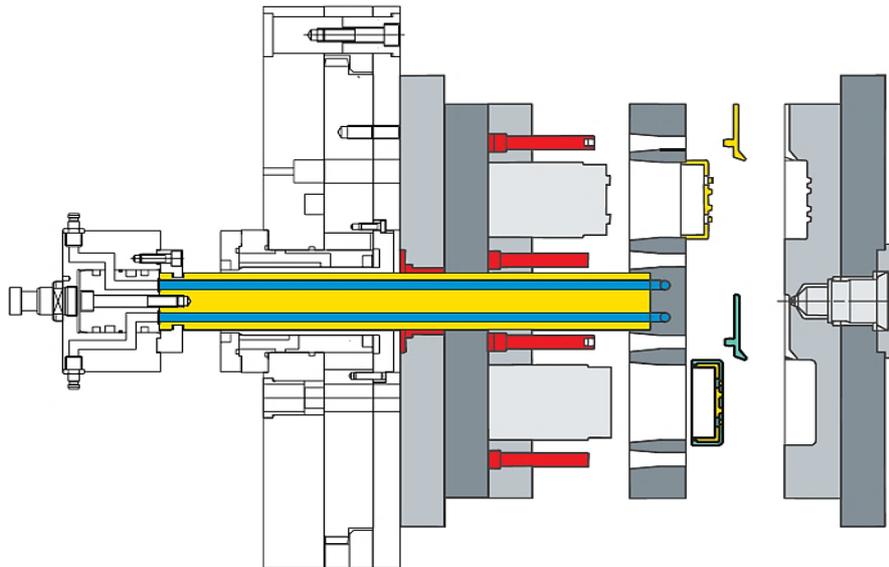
Molde bimaternal - rotação de uma placa do molde.
